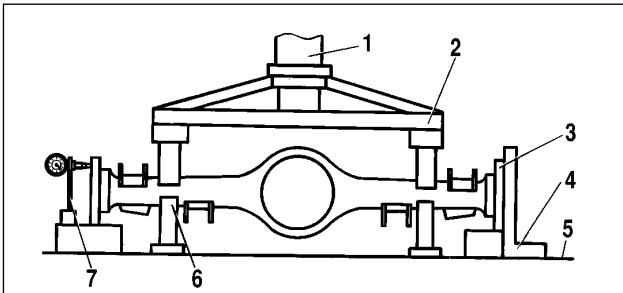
Schema zum Richten des Hinterachsträgers:
